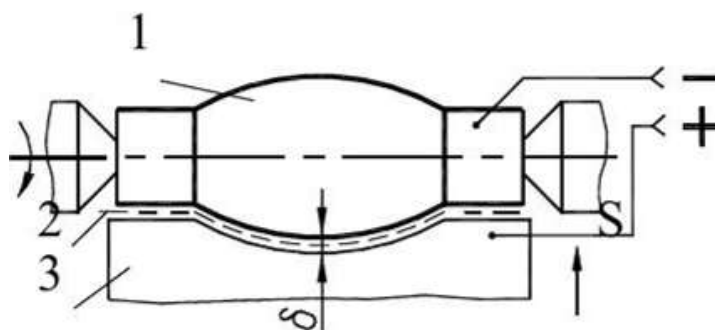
Схема електрохімічної обробки: 1 – заготовка; 2 – електроліт; 3 – електрод; δ - зазор між деталлю та електродом.
